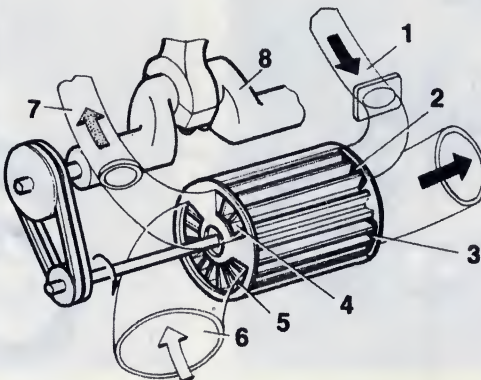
Нагнетатель «Компрекс»: 1 — выпускной трубопровод; 2 — окна для отработавших газов; 4 — окна для подачи сжатого воздуха; 5 — окна для свежего воздуха; 6 — патрубок подачи атмосферного воздуха; 7 — впускной трубопровод; 8 — коленчатый вал.
